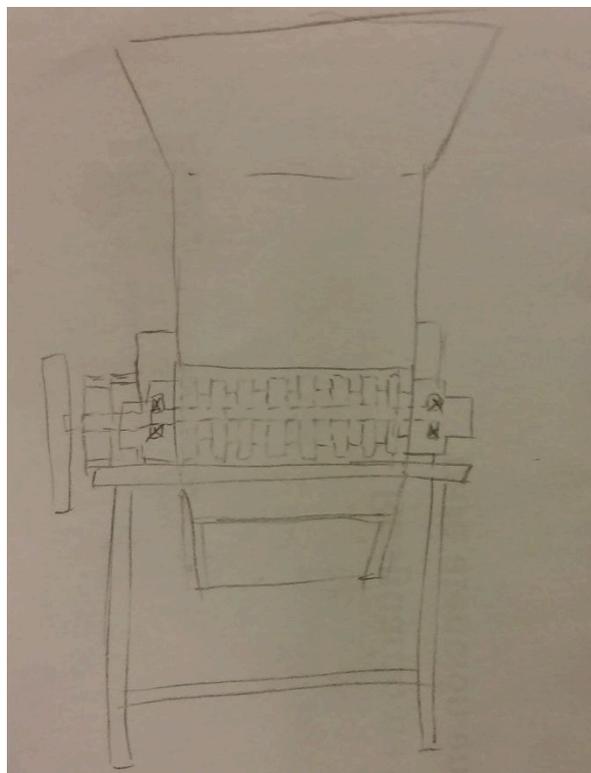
Vista de alzado de los elementos de la trituradora colocados en la mesa.
